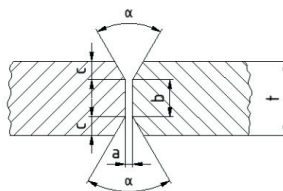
Nahtgeometrie einer zweiseitig ausgeführten Schweißnaht
